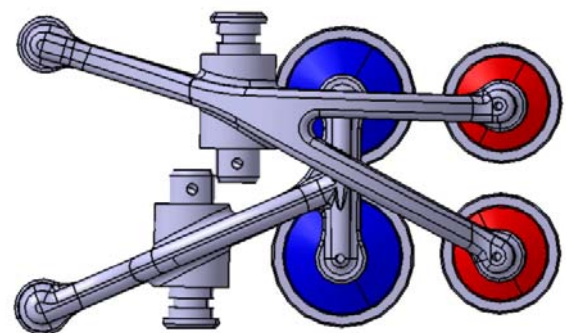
Vista dall'alto dei bilancianti.
